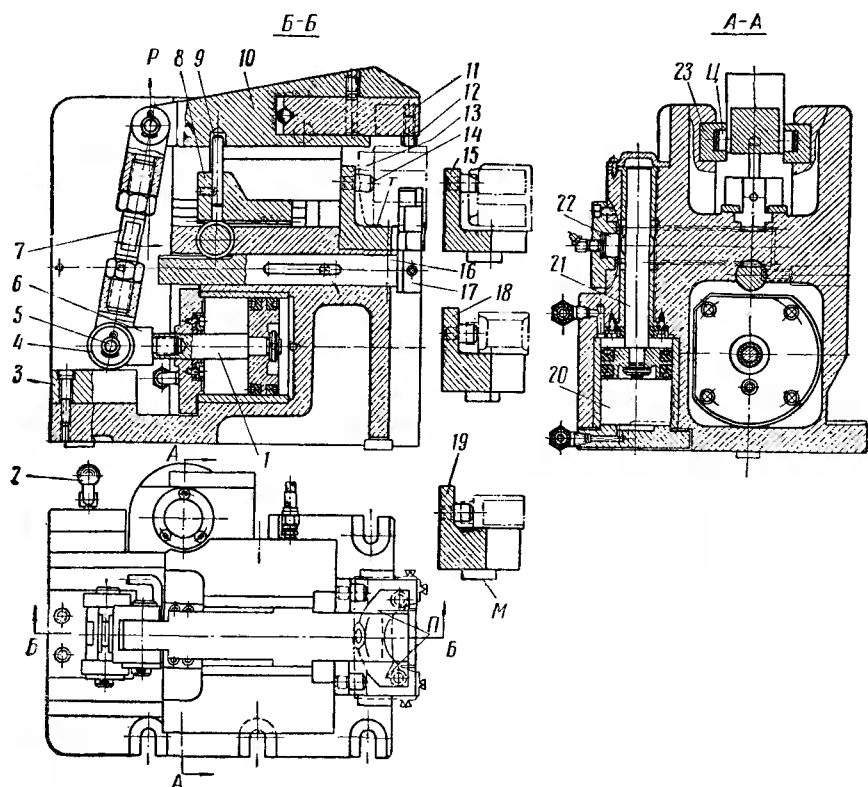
Приспособление для обработки протягиванием плоскостей стыка и установочных площадок крышек коренных подшипников
